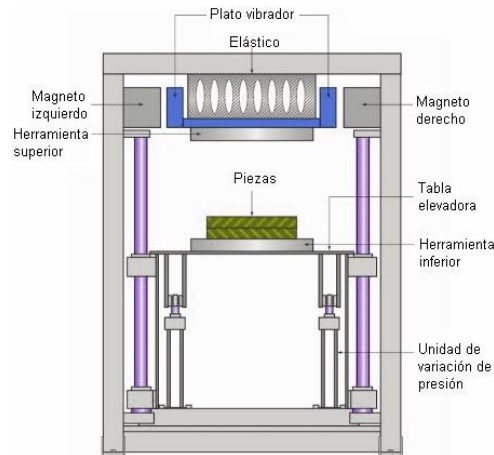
Esquema del equipo usado para la soldadura por vibración [10].
